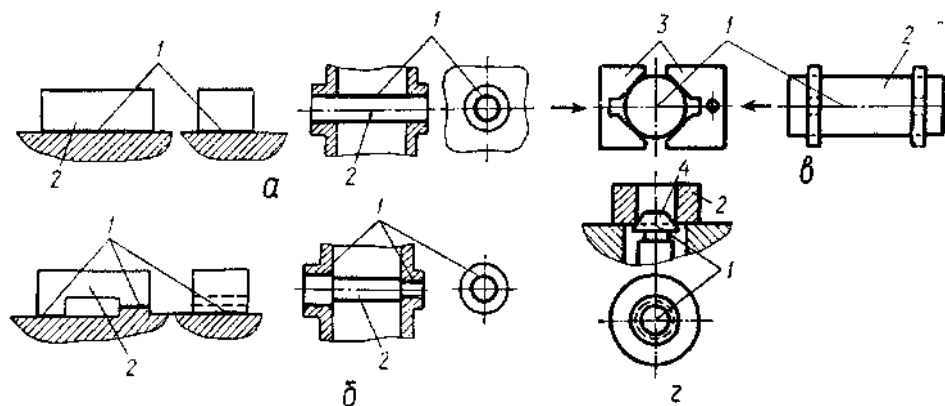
Приклади базування: 1 - база; 2 - заготовка; 3 - затискні губки; 4 - конус центрувального пристрою
